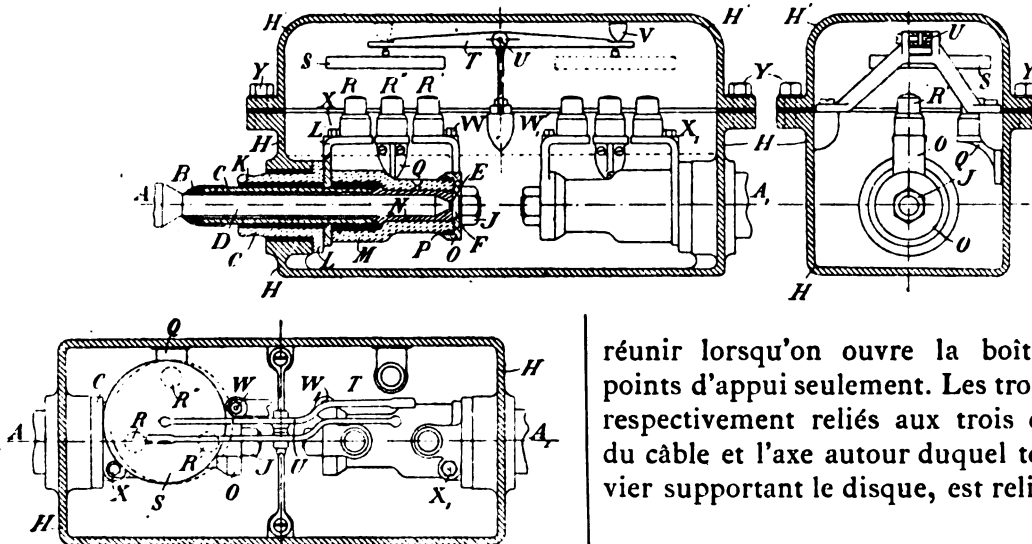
à 3. — Boîte de jonction Wordingham pour canalisations à haute tension. — Coupes longitudinale et transversale par un plan vertical et coupe longitudinale par un plan horizontal.
